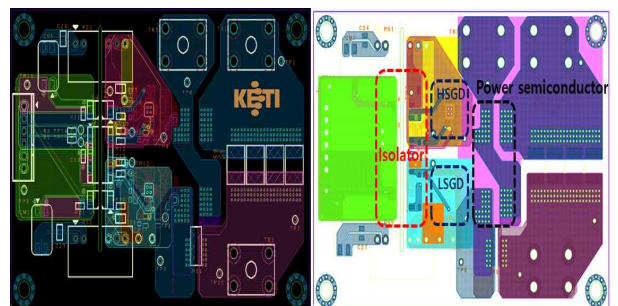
double pulse test 개발보드 회로도 및 PCB layout
